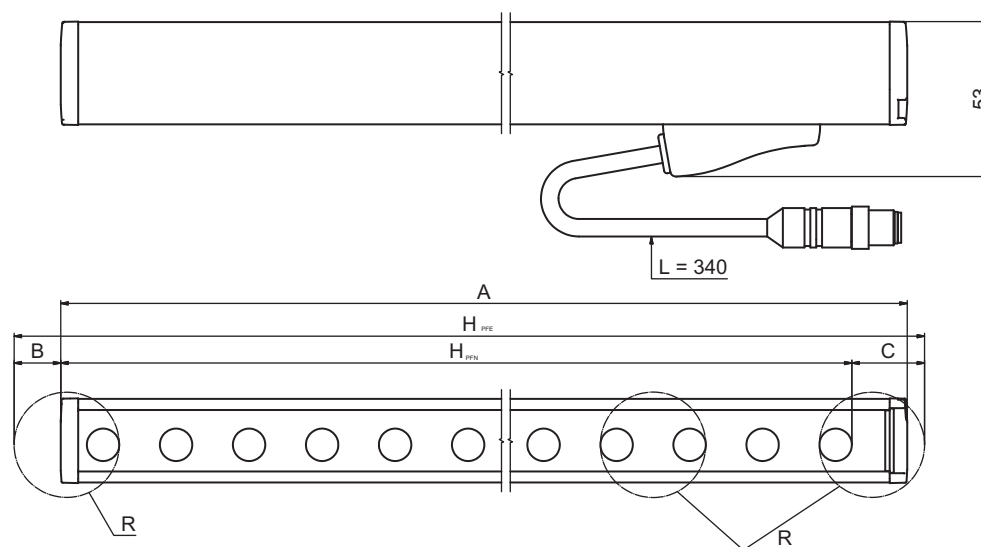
Dimensions de l'émetteur Guest et du récepteur Guest
